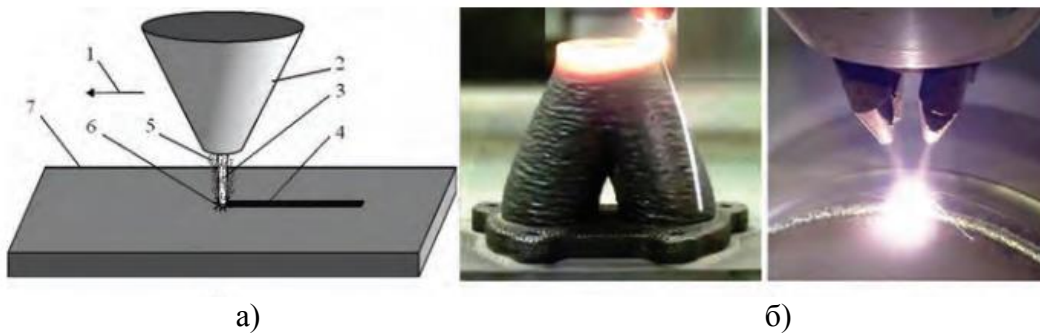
Спосіб 3D-друку металовиробів: а) принципова схема [3]:
